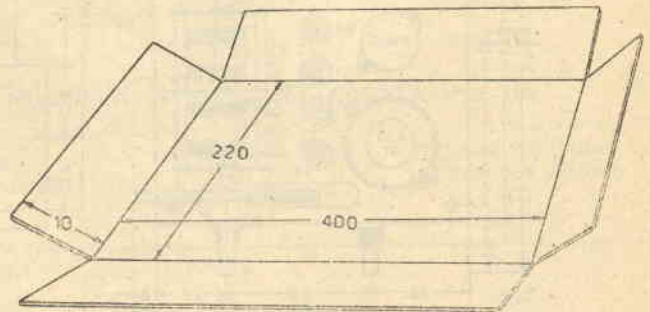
Dimensionamento telaio di montaggio per il complesso trasmettente.
